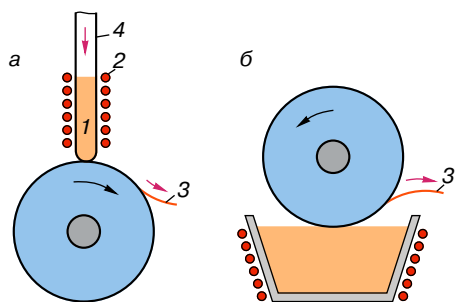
Схемы устройств для получения аморфных сплавов закалкой из жидкого состояния: а – нанесение расплава на вращающийся металлический диск или цилиндр; б – извлечение расплава вращающимся диском; 1 – расплав, 2 – нагревательное устройство (индукционная печь), 3 – лента аморфного сплава, 4 – кварцевая трубка
